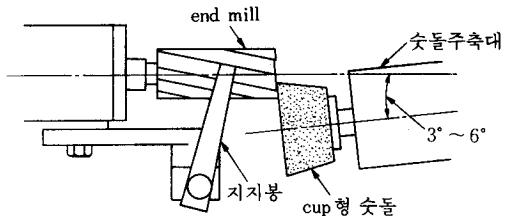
cup形 칫돌에 의한 end mill의연삭
